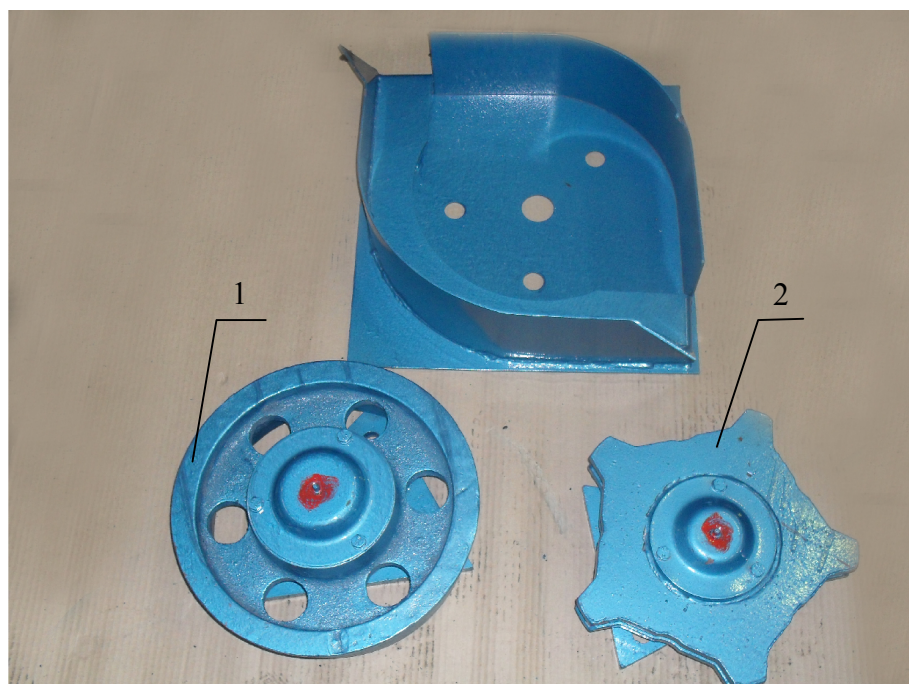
Поворотные устройства транспортера ТШ-300:
